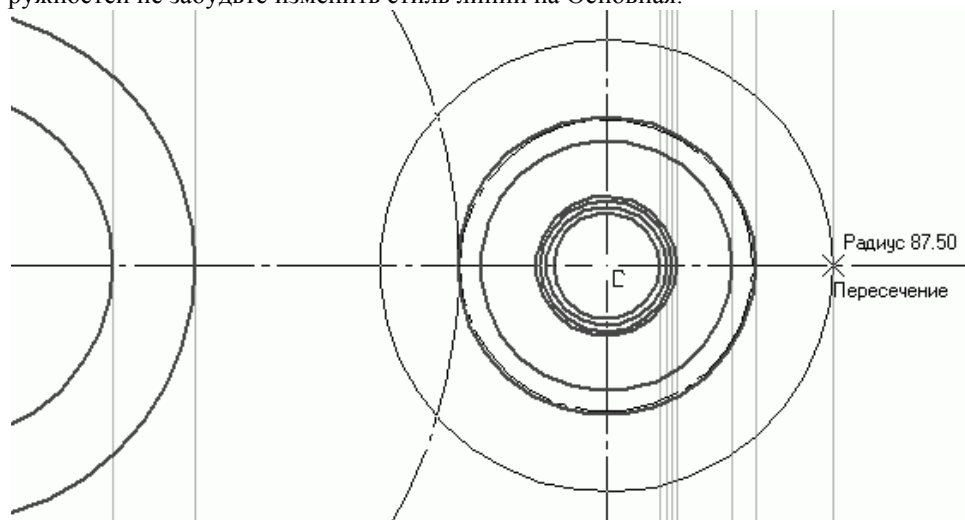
Процесс построения крышек подшипников и выходного конца ведущего вала
